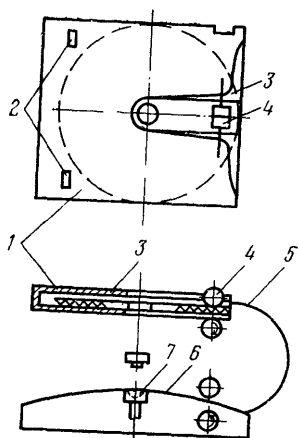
Устройство для извлечения видеопластинки из конверта.
